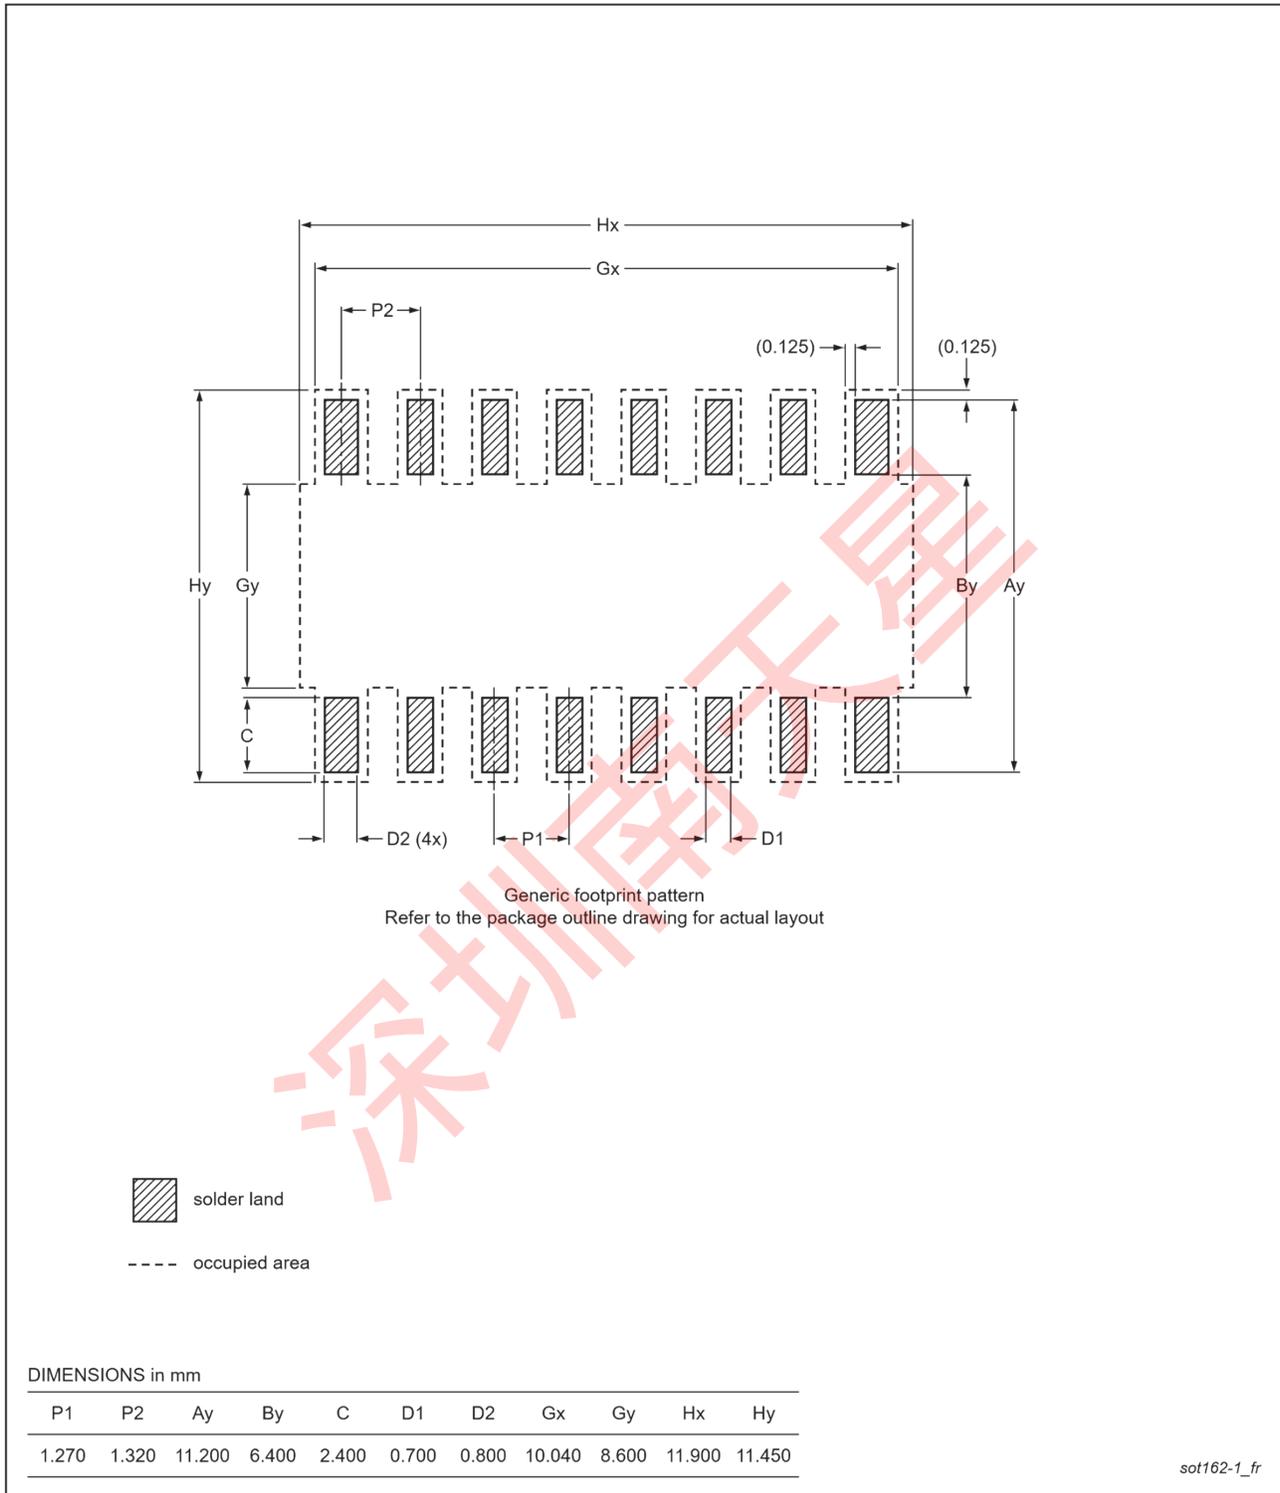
SOT162-1 (SO16) 的 PCB 占地面积; 回流 soldering
